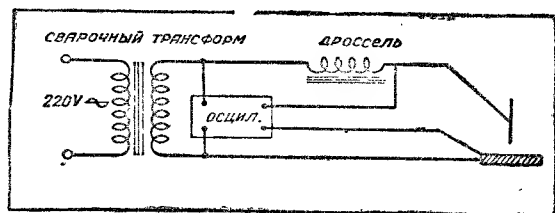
Принципиальная схема установки для дуговой сварки переменным током
